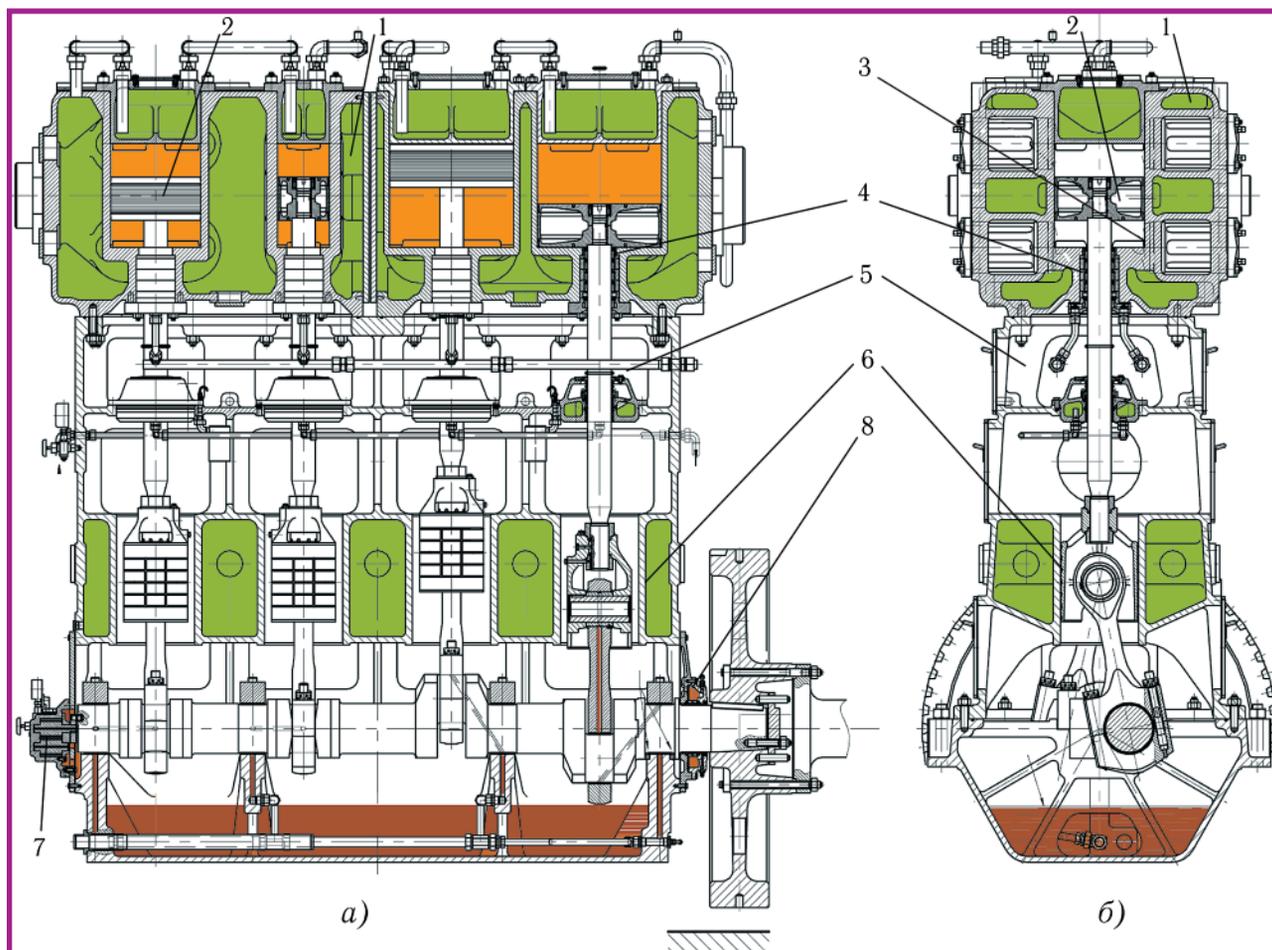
Кислородный компрессор 4D255-3D, продольный (а) и поперечный (б) разрезы: 1 — рубашка цилиндра для охлаждающей воды; 2 — лабиринтный поршень; 3 — клапан цилиндра; 4 — лабиринтный сальник штока поршня; 5 — разделительная секция увеличенной длины для отделения маслосмазываемого картера от несмазываемого цилиндра; 6 — направляющая крестовина с рубашкой для охлаждающей воды; 7 — масляный насос с приводом от коленчатого вала для принудительного смазывания подшипников и крестовины; 8 — уплотнение коленчатого вала.
